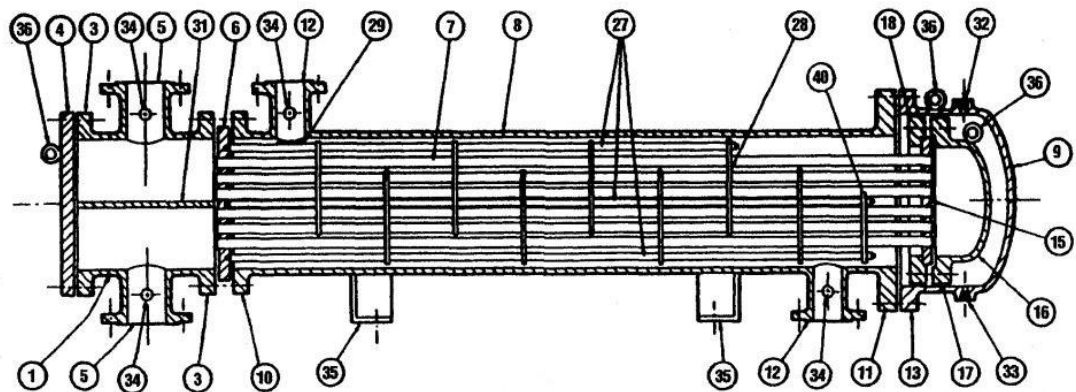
Principales componentes según norma de un intercambiador de calor de coraza y tubo. Fuente: [16]
